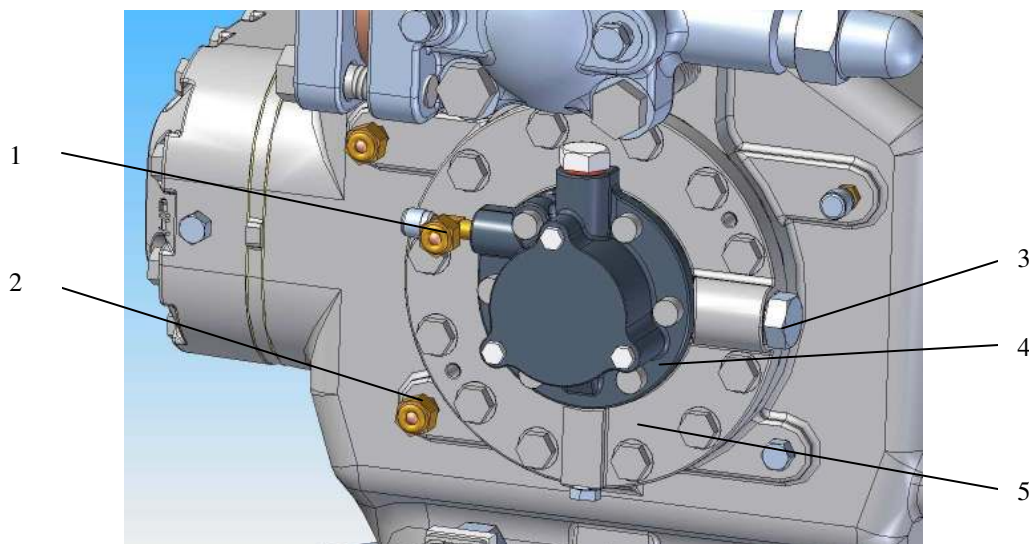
Модель компрессора SP4HF / SP4LF: шестеренный насос и предохранительный клапан
